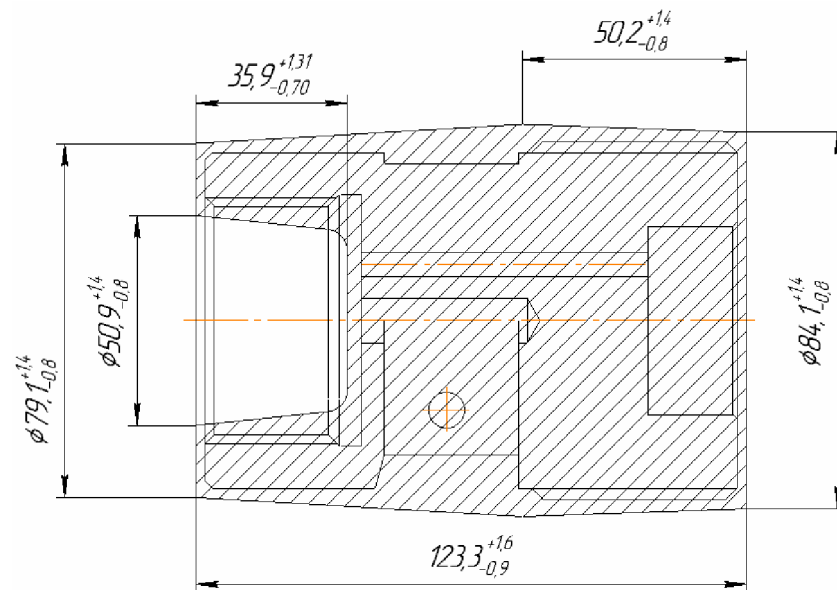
Ескіз заготовки, що виготовлена на КГШП
